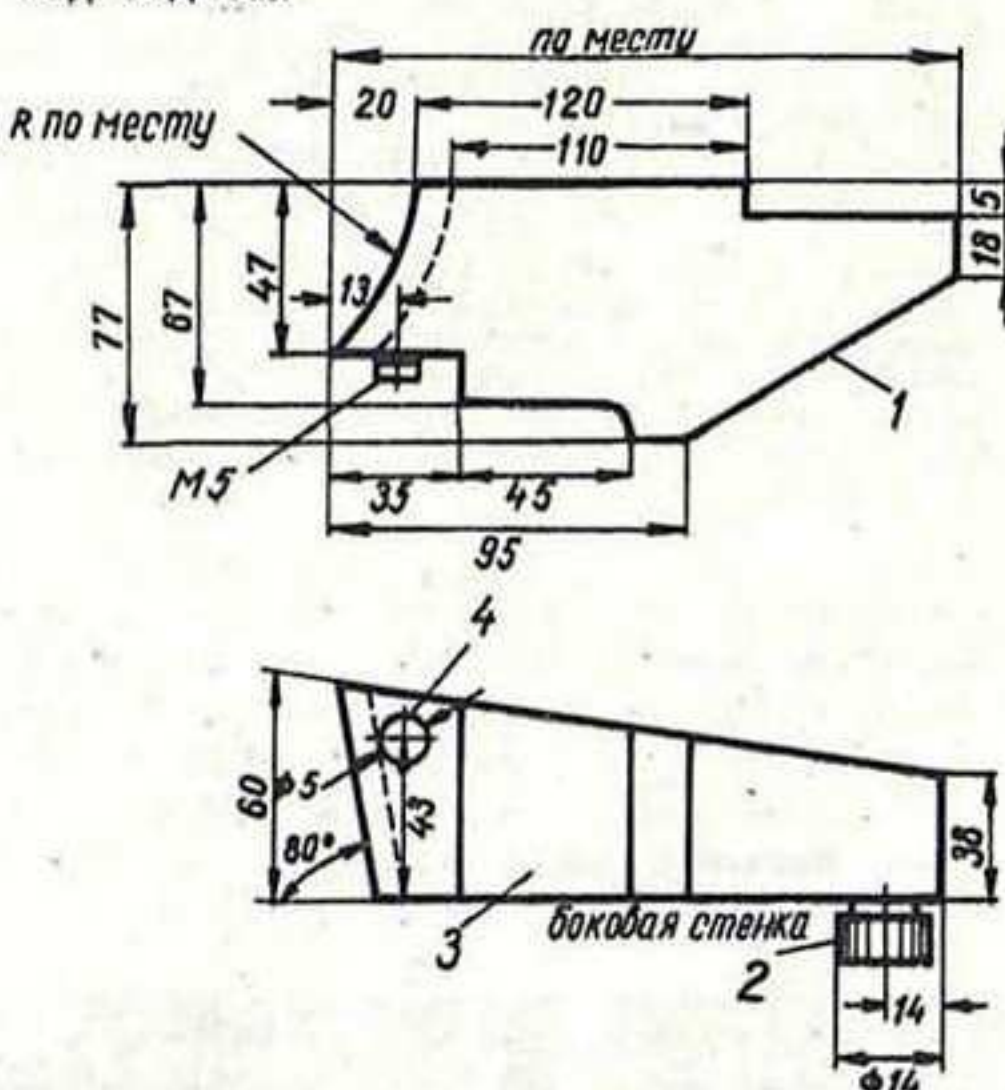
Размеры заготовок бачка: 1 — верхняя крышка; 2 — горловина с пробкой; 3 — боковая стенка; 4 — дополнительное отверстие.
